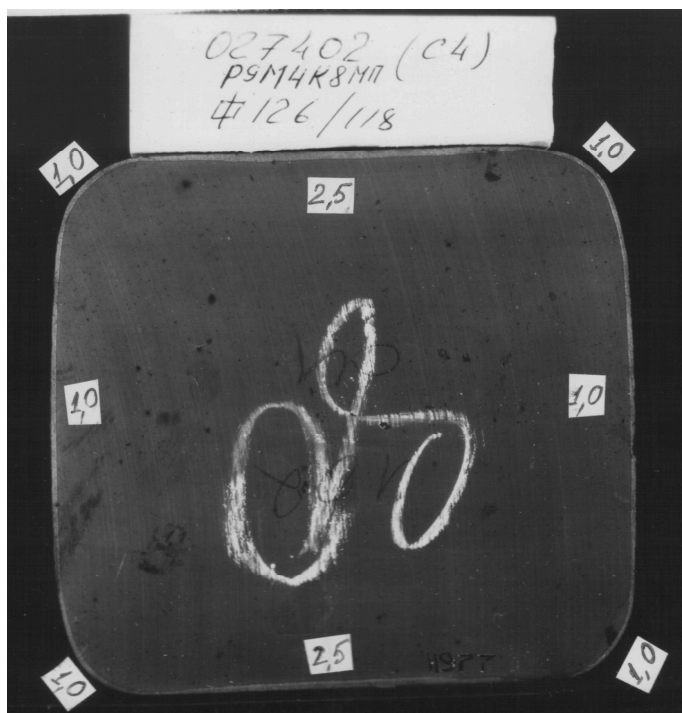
Распределение обечайки на поверхности катаной заготовки кв.126 мм стали Р9М4К8-МП.
